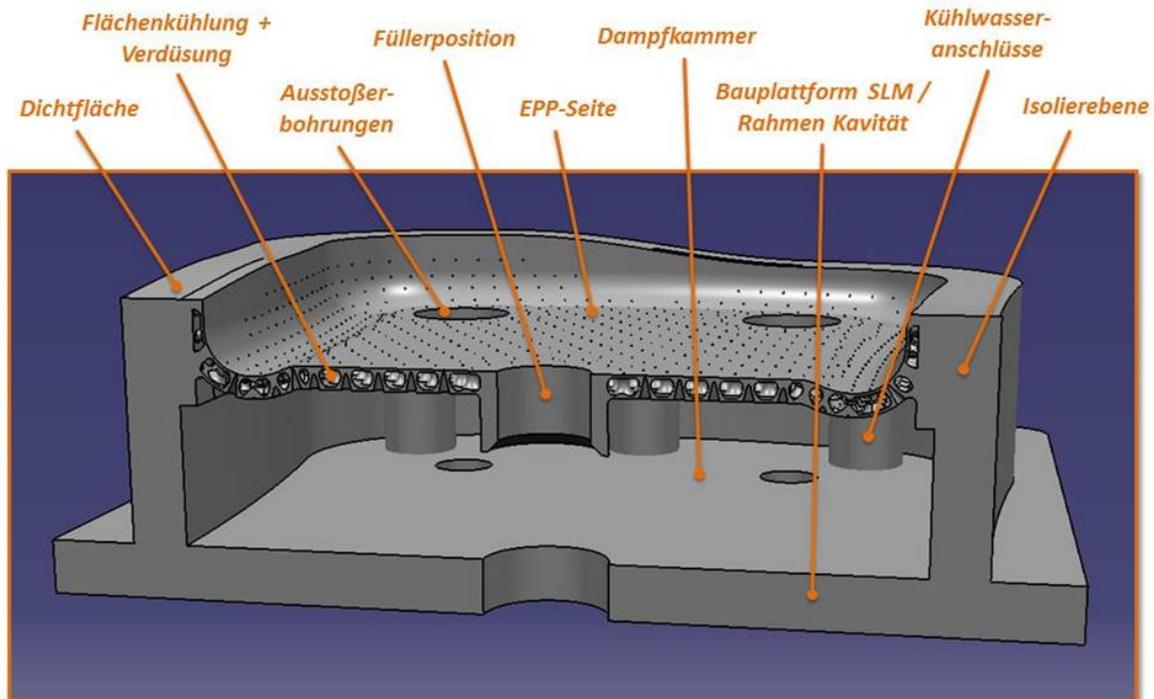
Schematische Abbildung eines gedruckten Werkzeuges
